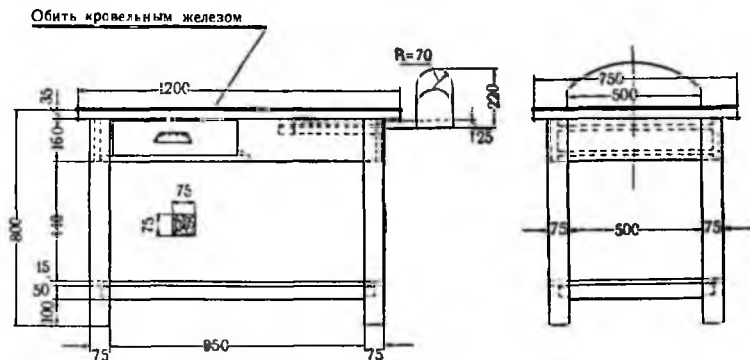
Стол для обрезки повреждений покрывок и для заготовки манжет.
